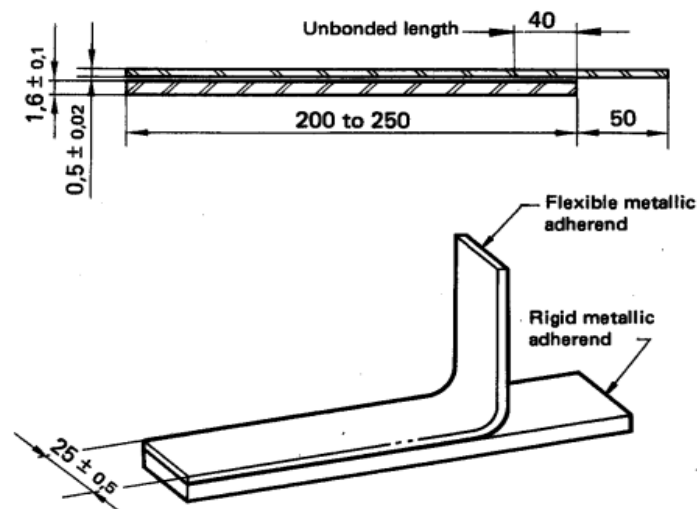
Dimensões do provete para ensaio *floating roller peel* [49]
